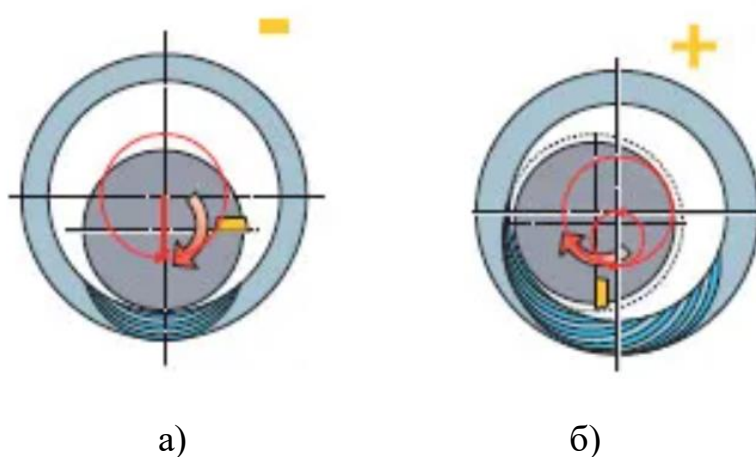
Схеми врізання фрези у заготовку а) при прямому врізанні; б) із переміщенням фрези по додатковому колу в процесі врізання [12]
